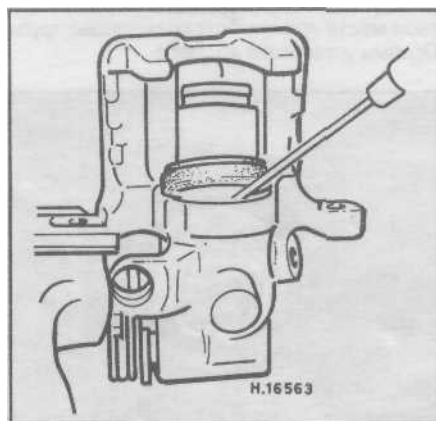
Установка внутренней кромки уплотнения защитного колпачке в канавку цилиндра
